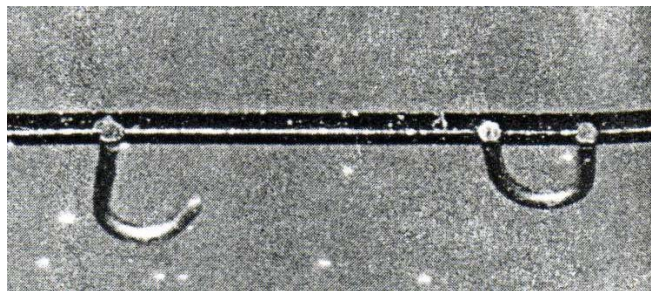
การเชื่อมแบบเป็นจุด (resistance spot welding)<sup>56</sup>
